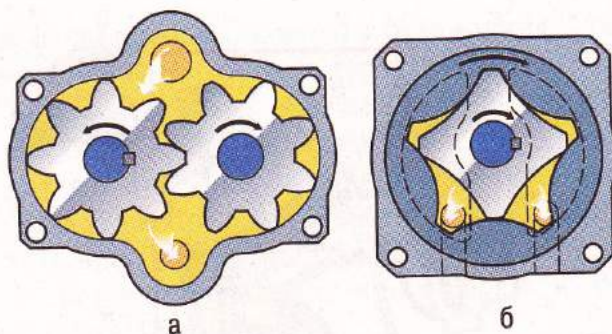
Типы масляных насосов: а – шестеренный с наружным зацеплением шестерен; б – с внутренним зацеплением шестерен
